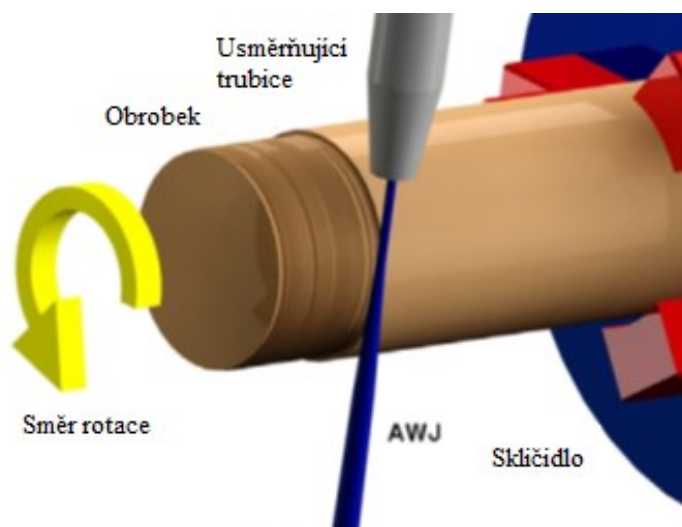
Dopadový úhel pro tangenciální režim souběžného soustružení abrazivním vodním paprskem [14]
